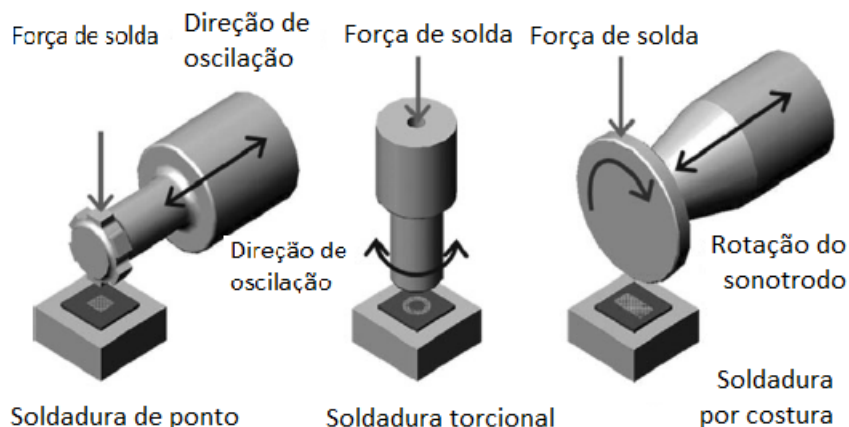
Variantes do processo de soldadura por ultra-sons. Adaptado de: [15]
